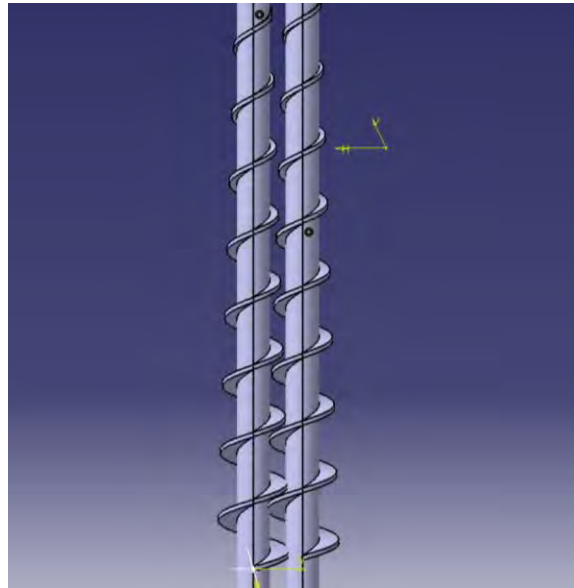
Vista superior del mecanismo de doble tornillo sin fin (realizado en Catia V5)
